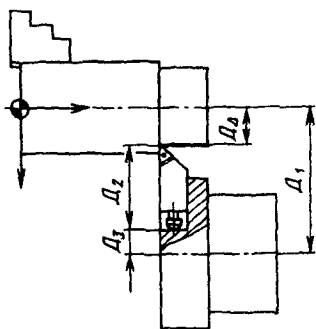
Размерная цепь образования радиуса детали при обтачивании
